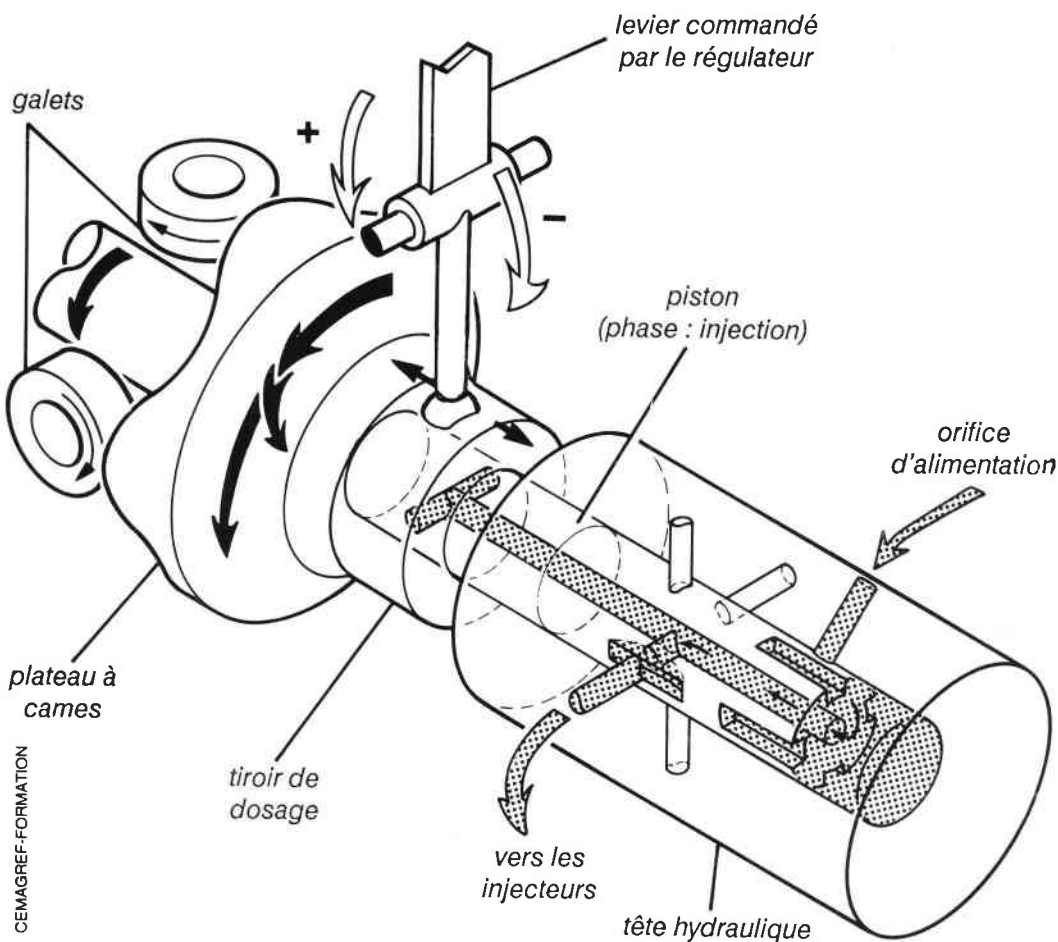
Principe de la pompe d'injection rotative Bosch, type EP/VE.
